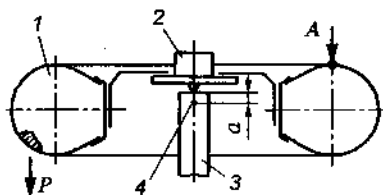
Статическая балансировка колеса: a — расстояние от центра тяжести колеса до опорной поверхности; 1 — колесо; 2 — приспособление; 3 — опора; 4 — центр тяжести колеса
